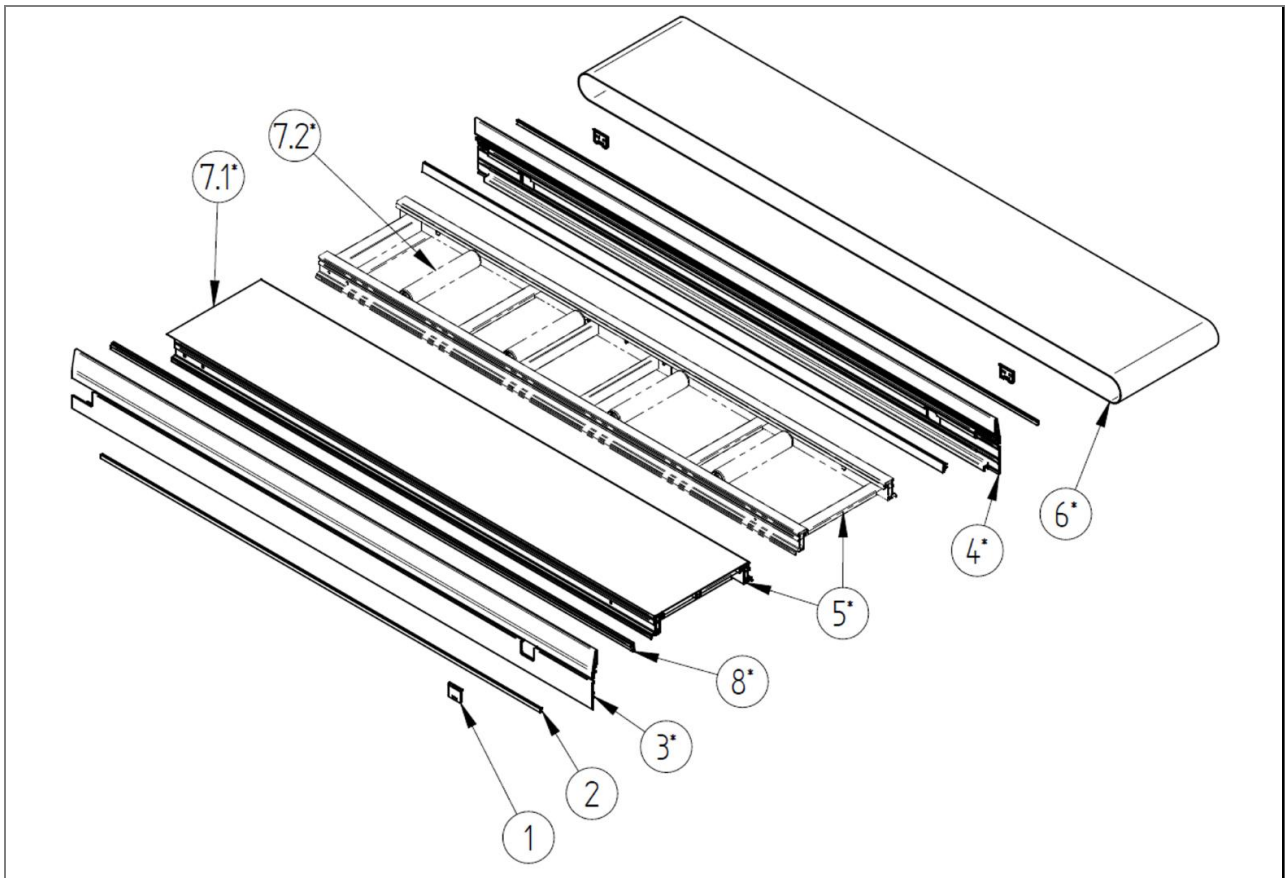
Lista de piezas del cuerpo de la cinta transportadora GL40; GL80; GL80A - U.116.0003.00
